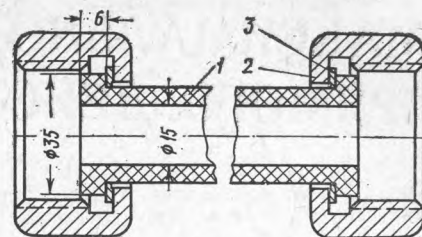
Полиэтиленовый шланг с металлической арматурой:
